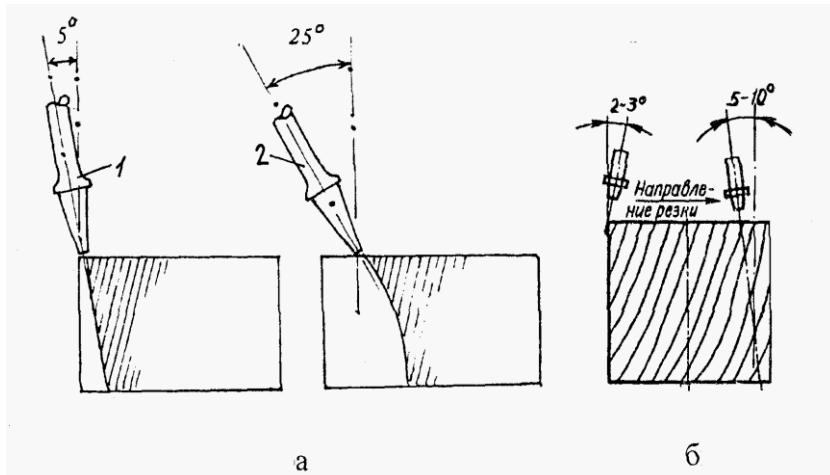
Техника резки: *a* – листового металла; *б* – металла большой толщины (*1* – начало резки; *2* – конец резки)
